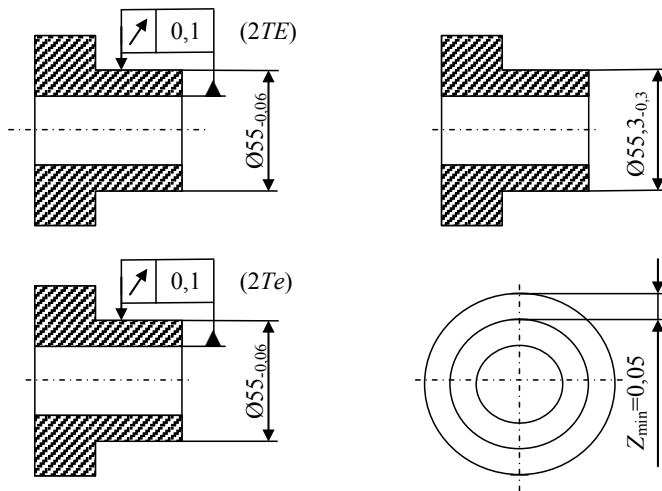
а* – эскиз детали; *б* – эскиз заготовки; *в* – эскиз механической обработки; *г* – схема снятия равномерного припуска
